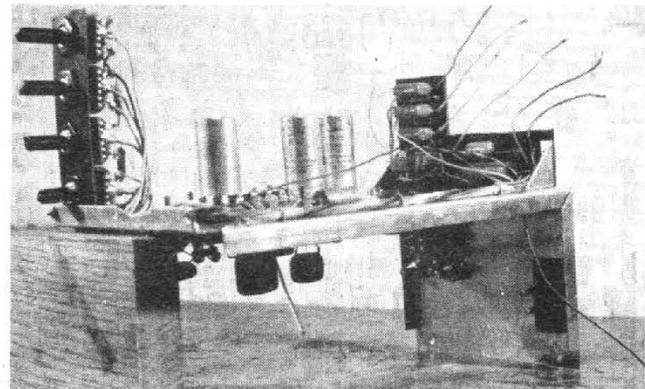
Autre vue du dessus de B, la pièce D enlevée, on distingue beaucoup mieux les R et C de la plaquette E. Remarquer que la résistance R_6 n'est pas soudée.
